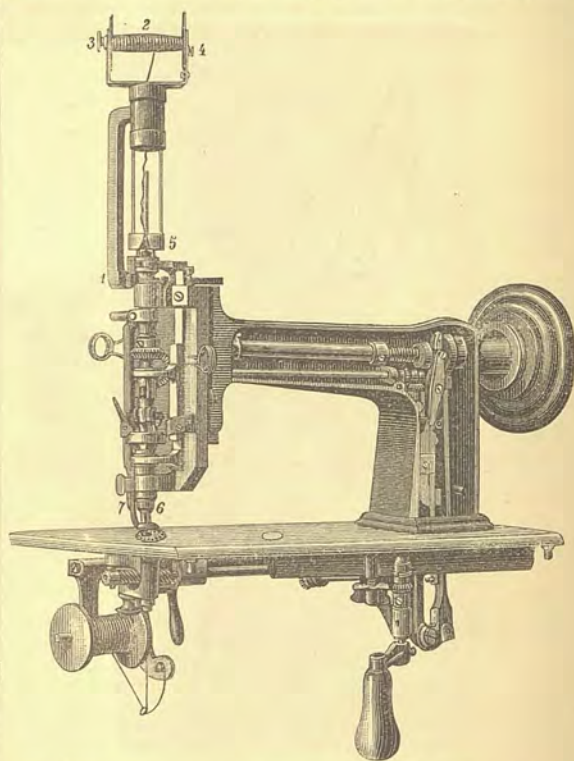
Macchina a ricamare con spinetta od a spinettare.
